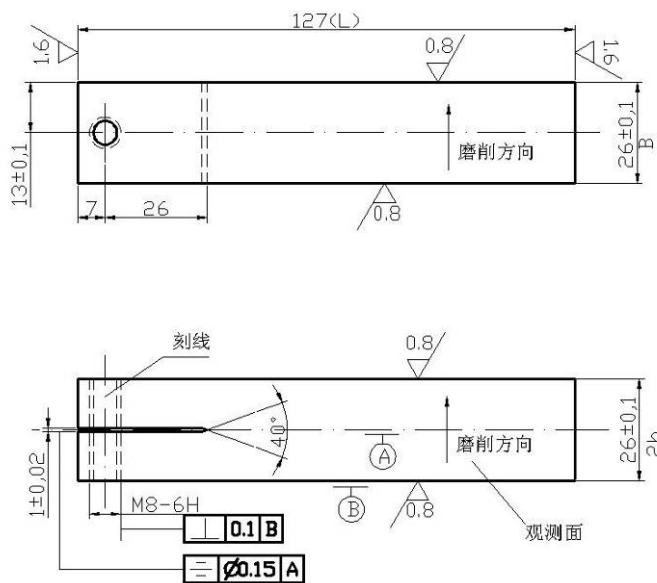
推荐的铝合金 DCB 试样的形状和尺寸
